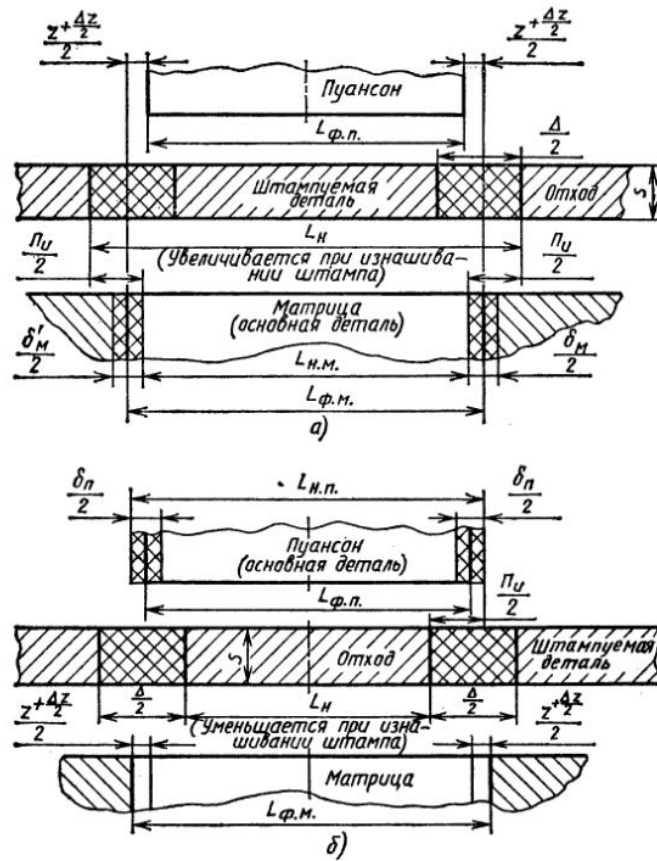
Схема размеров и полей допусков штампуемой детали и рабочих деталей штампа при их совместном изготовлении: а – при вырубке; б – при пробивке; L_n – номинальный размер штампуемого элемента; $L_{н.м.}$ – номинальный размер матрицы; $L_{н.п.}$ – номинальный размер пуансона; $L_{ф.м.}$ – фактический размер матрицы; $L_{ф.п.}$ – фактический размер пуансона; Δ – допуск размера штампуемого элемента; Π_u – припуск на изнашивание пуансона и матрицы; Δ_n и Δ_n – допуски размеров пуансона и матрицы; Z и ΔZ – зазор и поле допуска зазора между матрицей и пуансоном (двусторонние).
